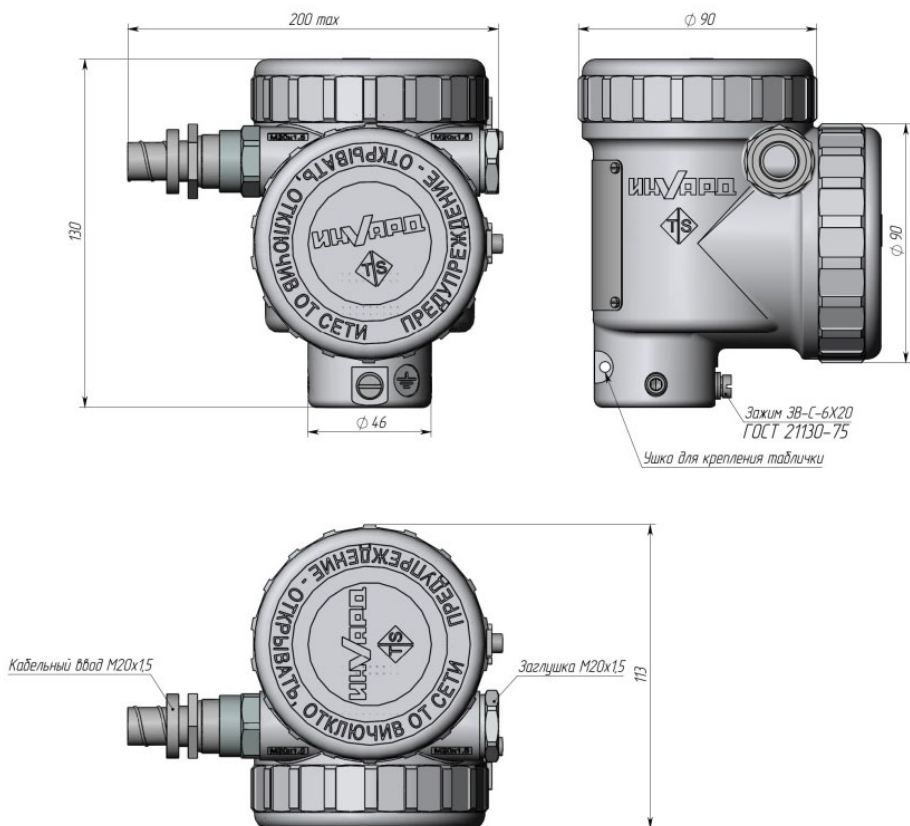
Габаритные и установочные размеры алюминиевого мини корпуса блока электронного преобразователя. IP68
